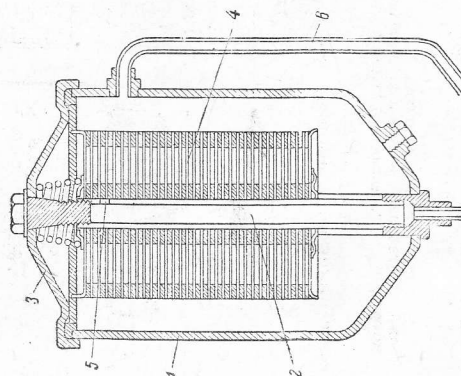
Фильтр тонкой очистки: 3 — корпус; 2 — центральная трубка; 3 — крышки; 4 — фильтрующий элемент; 5 — калиброванное отверстие центрального трубки; 6 — трубка, подводящая масло.
